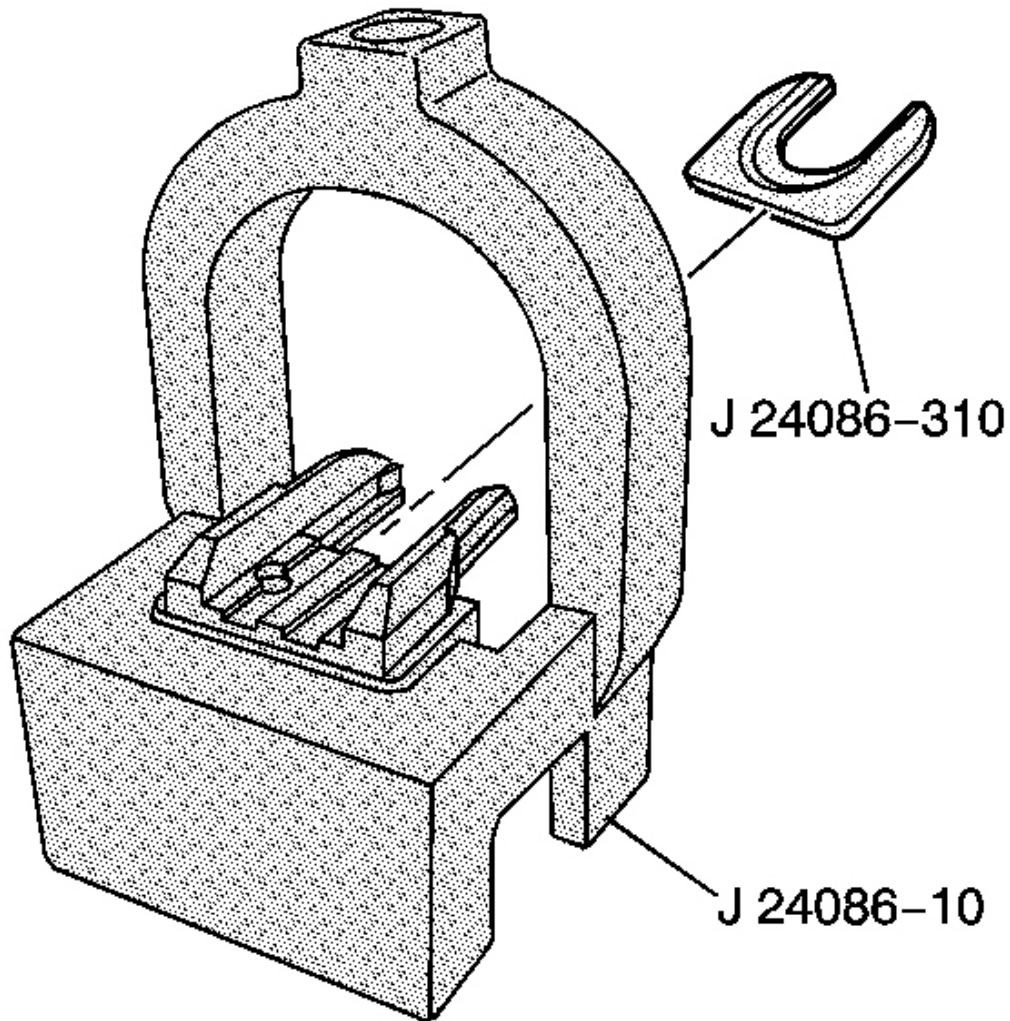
Vista de Montaje / desmontaje de los anillos de pistón
